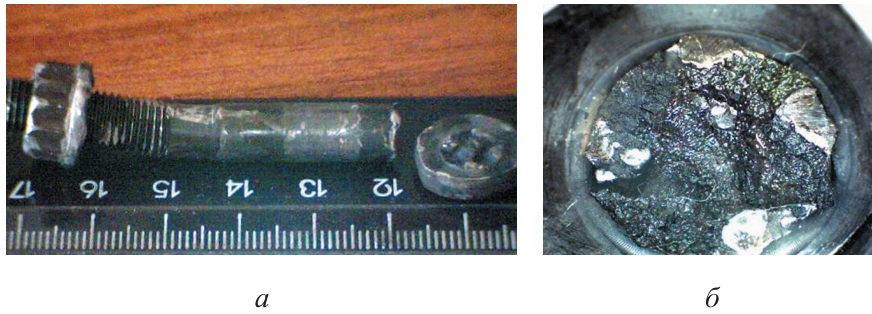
Внешний вид разрушенного ШБ (а) и поверхности его излома (б)
